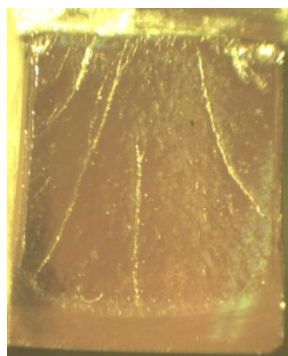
Superficie de fractura de una probeta grupo 2.
